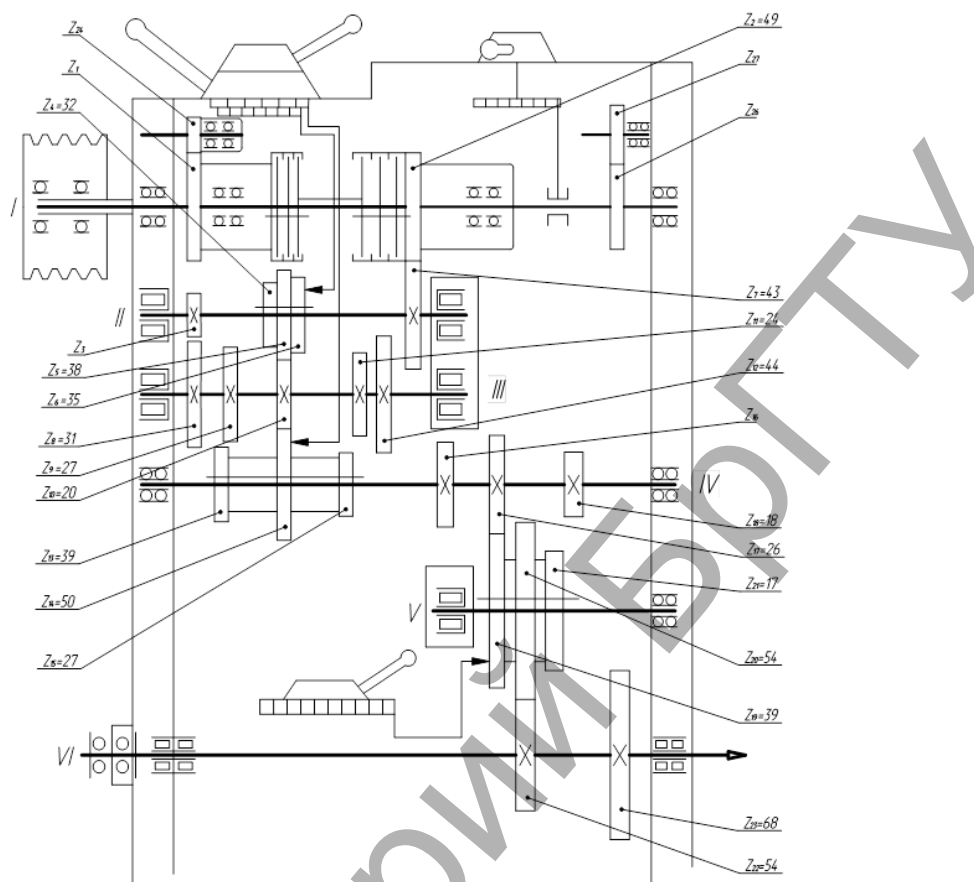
Кинематическая схема коробки передач универсального токарного станка СН-501
